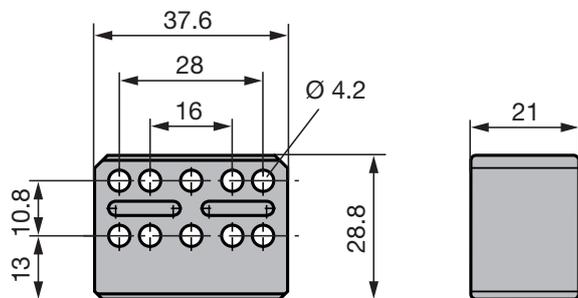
Medidas de montaje del sensor de posición BTL6-A-3800-2
